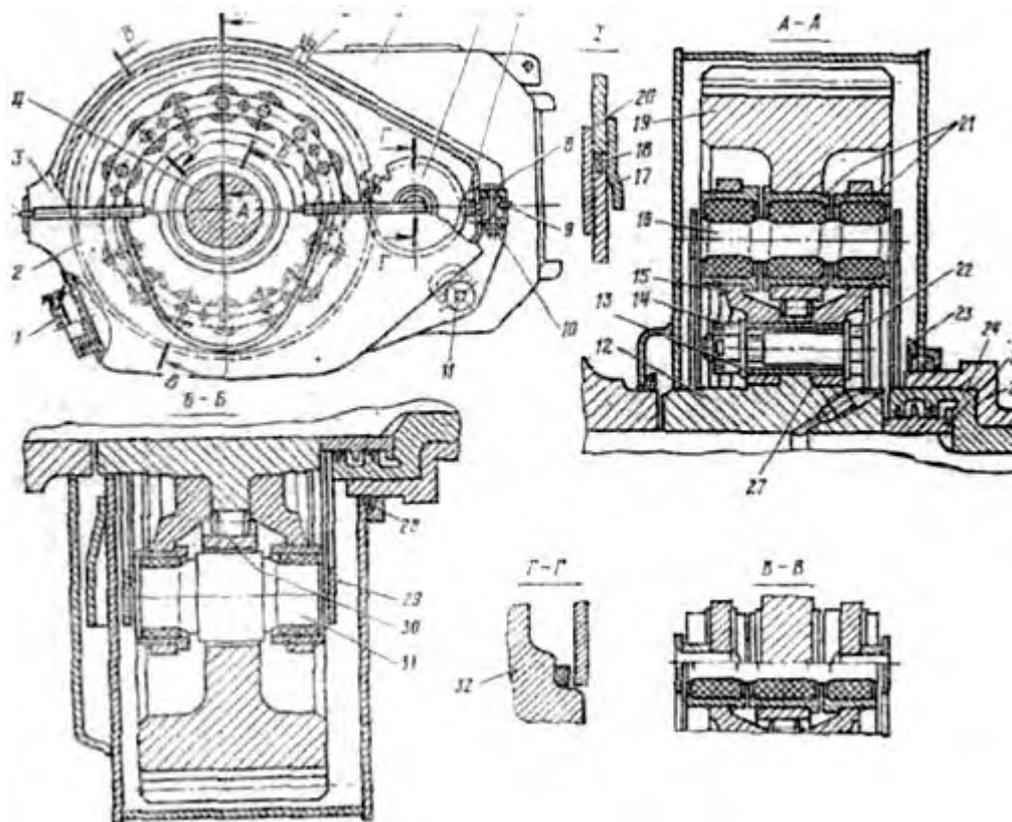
Тяговый редуктор (Двигатель ЭД118Б):
